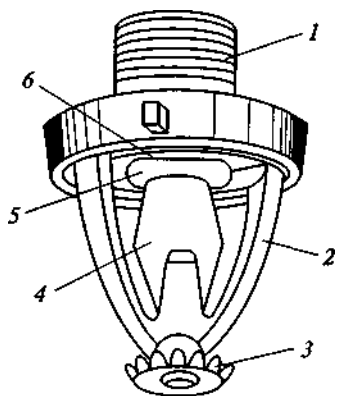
Спринклерная головка: 1 — головка корпуса; 2 — рамка; 3 — розетка; 4 — пластины замка; 5 — стеклянный клапан; 6 — диафрагма
